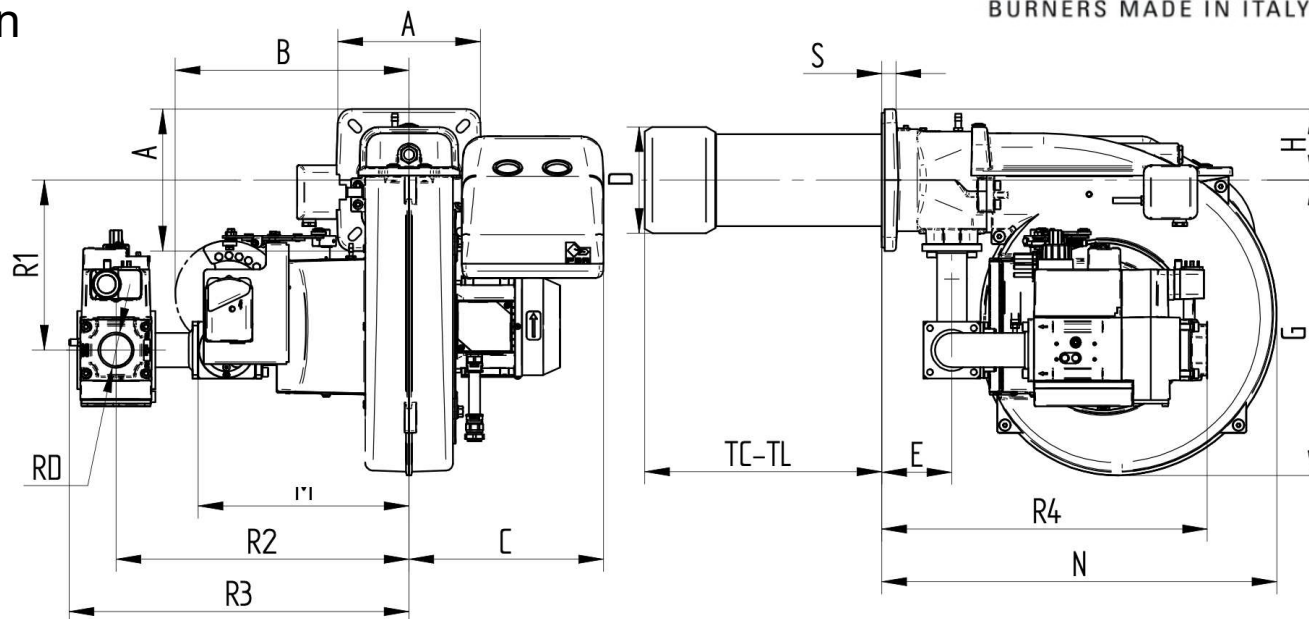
Dimensioni ingombro GAS XP60/MCE-EVO
